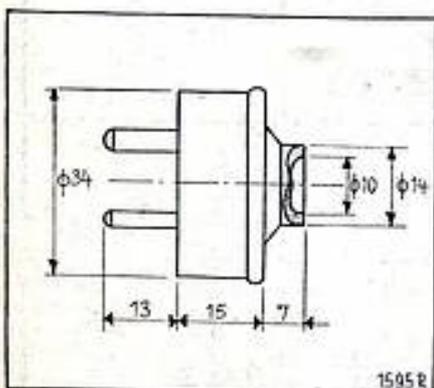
Dimensions des bouchons 1904 et 1905.
